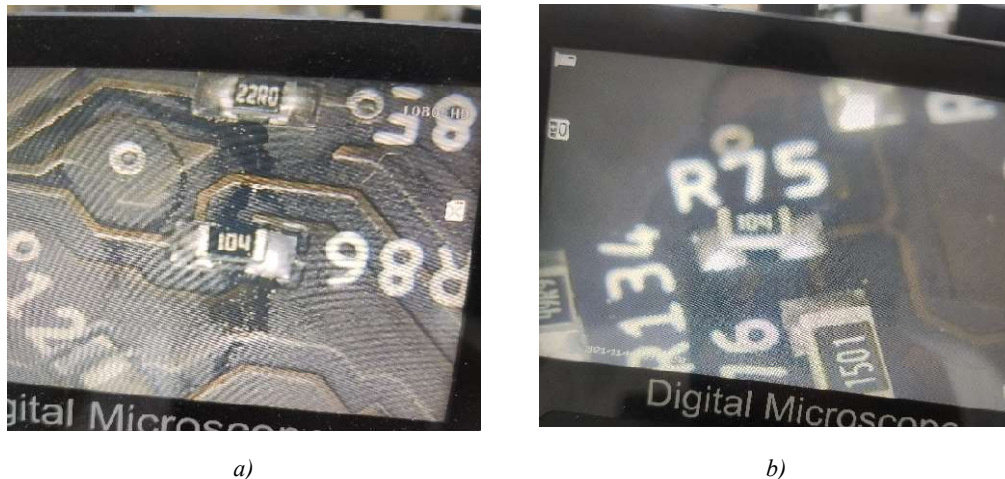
Verificação de soldaduras nas placas PCB: soldaduras deficientes.
